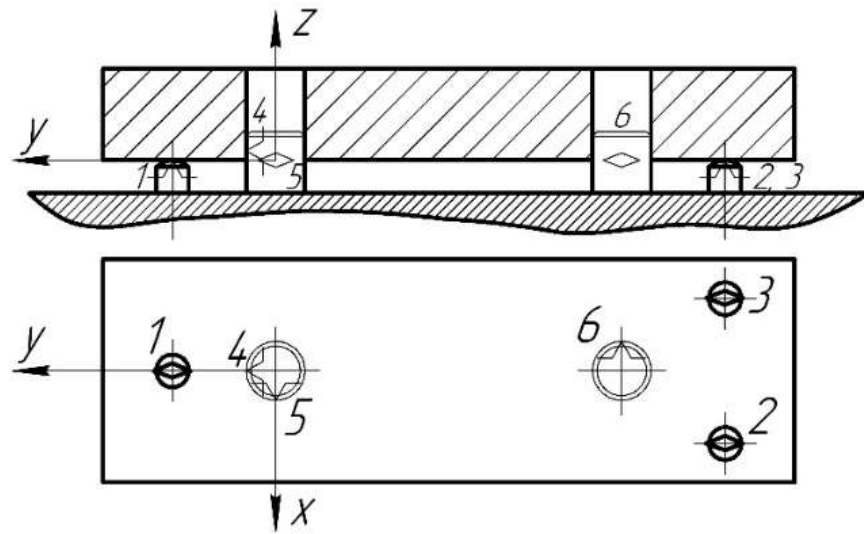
Установка заготовки на два циліндричні пальці.
